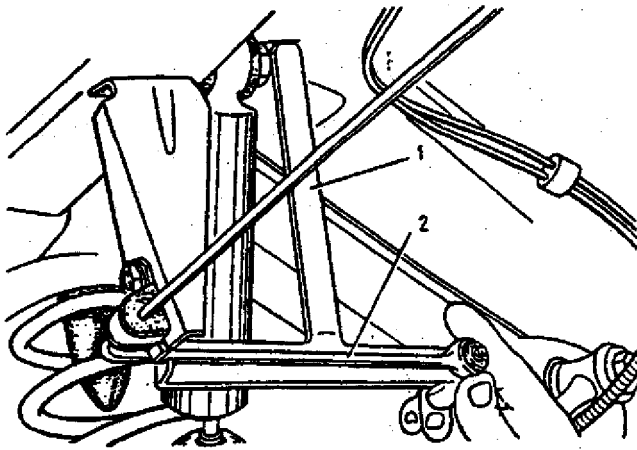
Instalação do dispositivo de ajuste; 1 - dispositivo 67.7820-9519; 2 - alavanca de acionamento do regulador de pressão.
